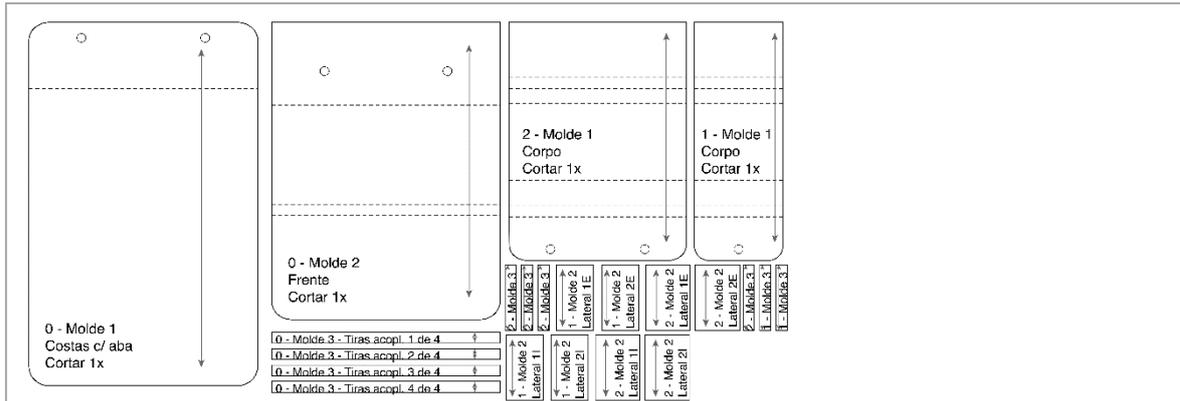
Plano de corte - Cortiça JPS Cork (Fonte: Autor)
